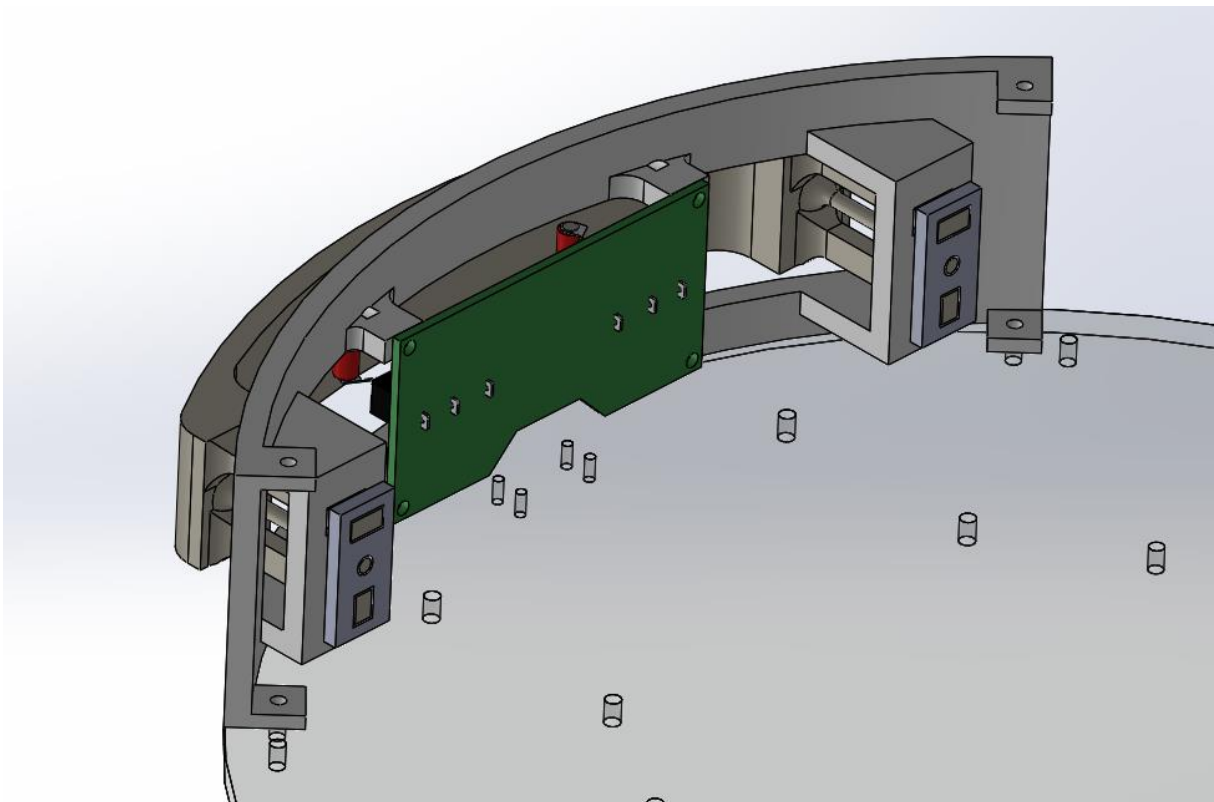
assemblage paroi bumper bloqueur et PCB interrupteur
